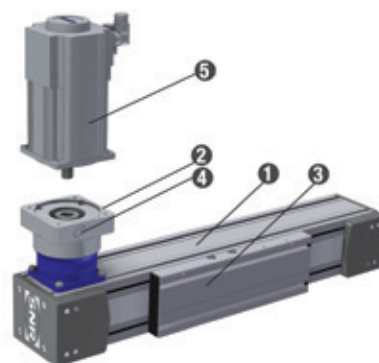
Motormontage an Linearachsen Planetengetriebe
